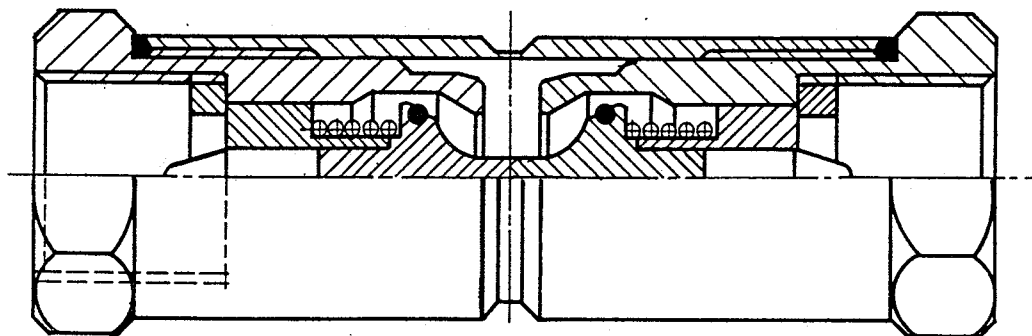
Diferenciálny ventil DN 25 s obmedzovačom prietoku
